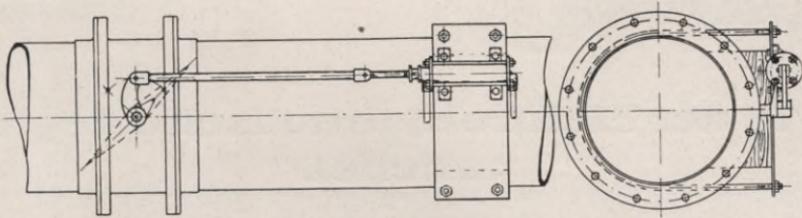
Befestigung des Stellzylinders an der Rohrleitung.
